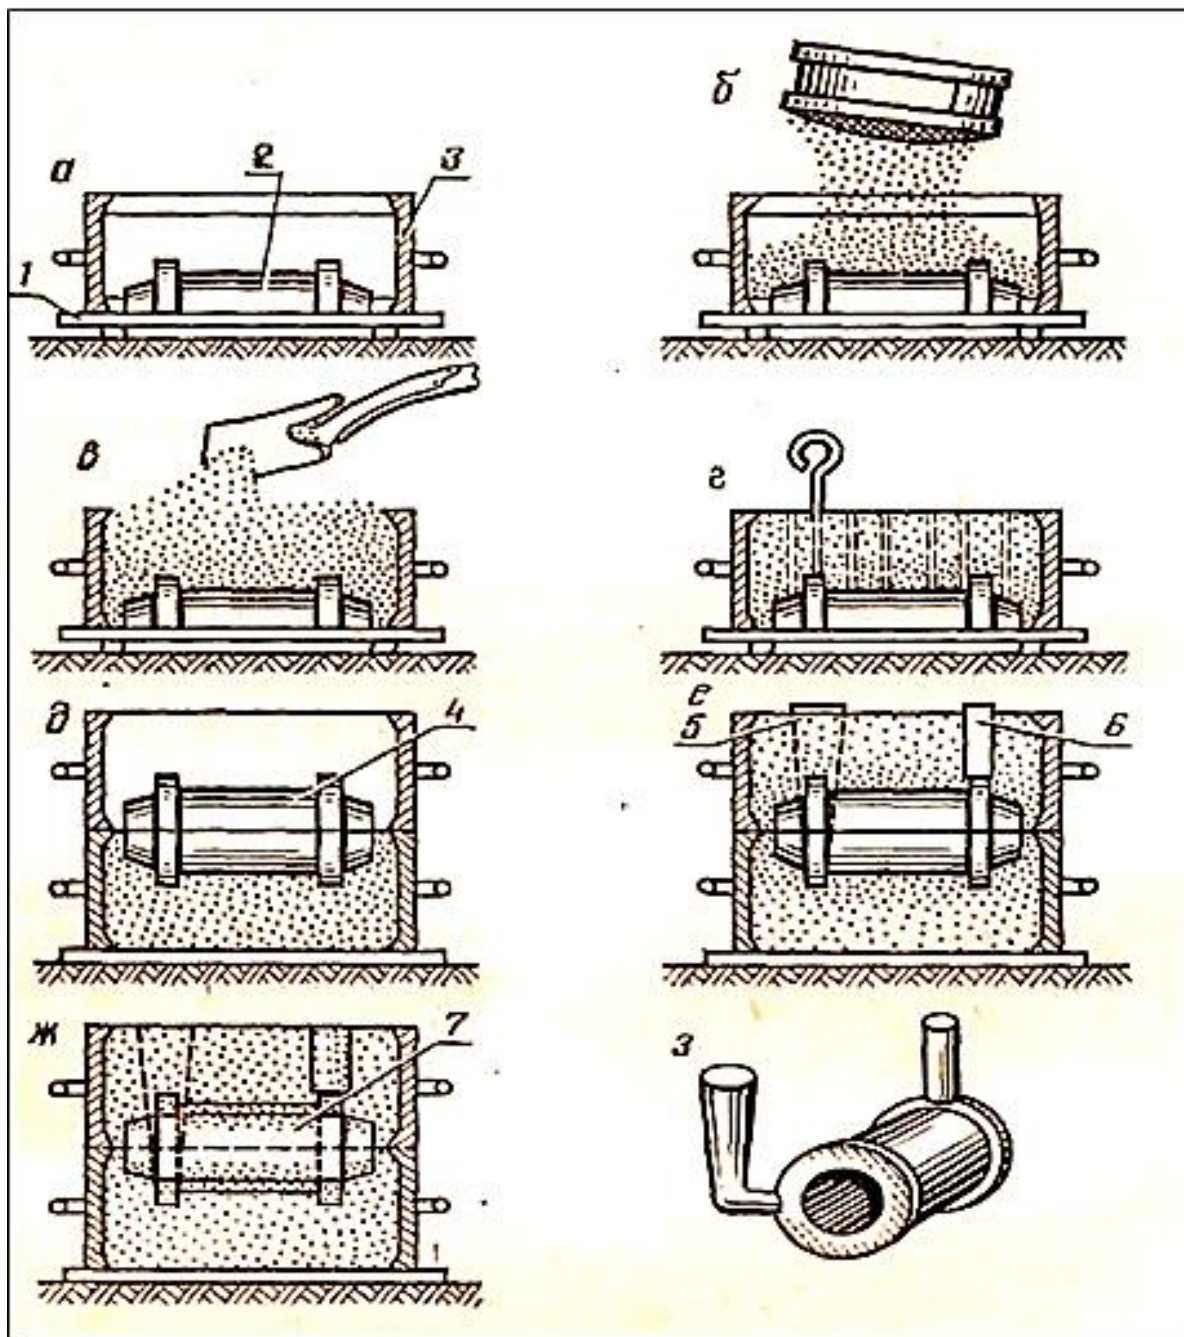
Схема изготовления литейной формы ручной формовкой в двух опоках: 1 – подмодельная доска; 2 – половина модели отливки; 3 – опока нижняя; 4 – вторая половина модели; 5 – стояк; 6 – выпор; 7 – стержень; а – ж – изготовление литейной формы; з – отливка с элементами литниковой системы
